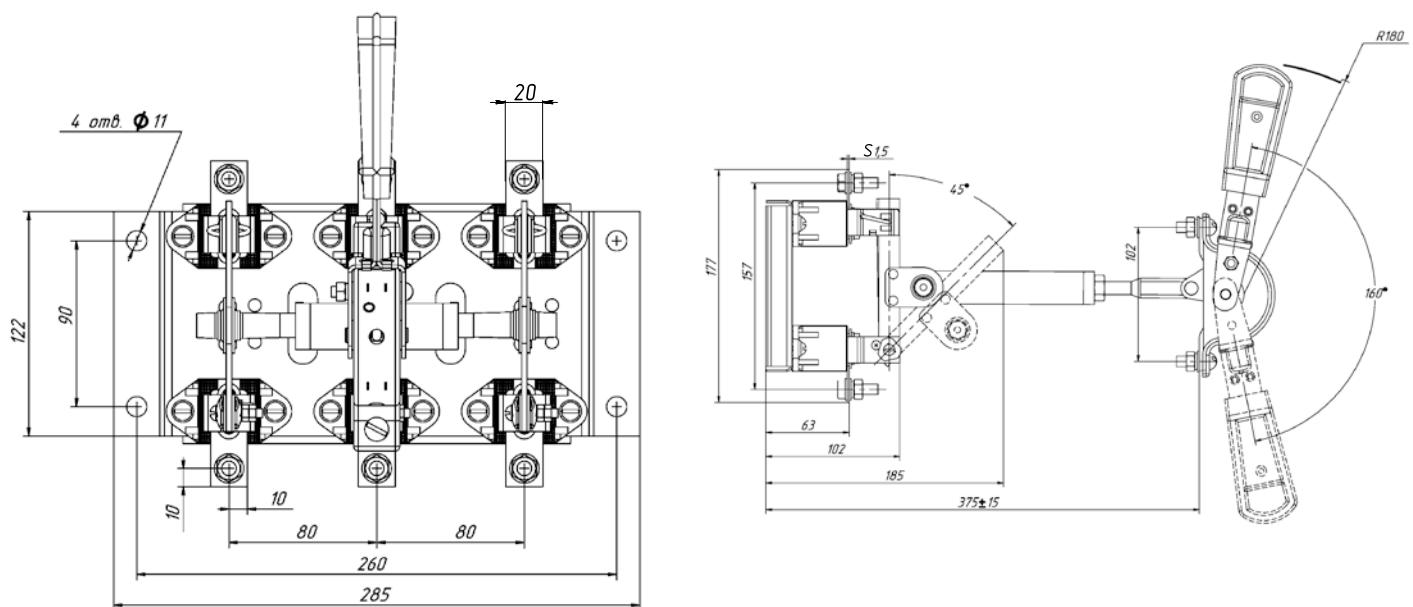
Разъединитель серии Р с центральным приводом РЦ-1,
